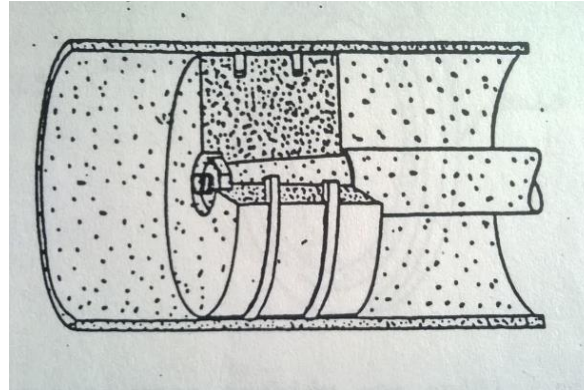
Anillos del pistón con tolerancia baja de contacto.
